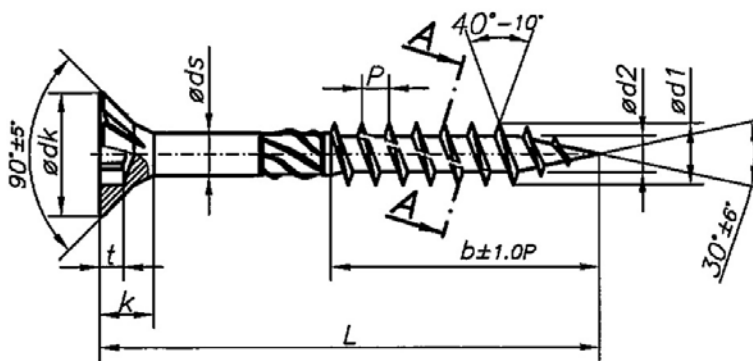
Skizze der verwendeten Holzbauschraube [28]
